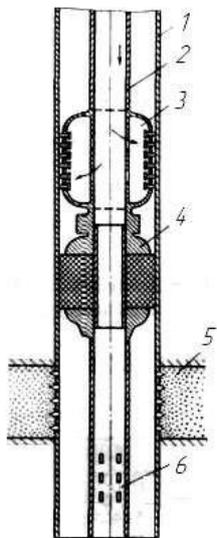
Розташування пакера і якіря в свердловині:
